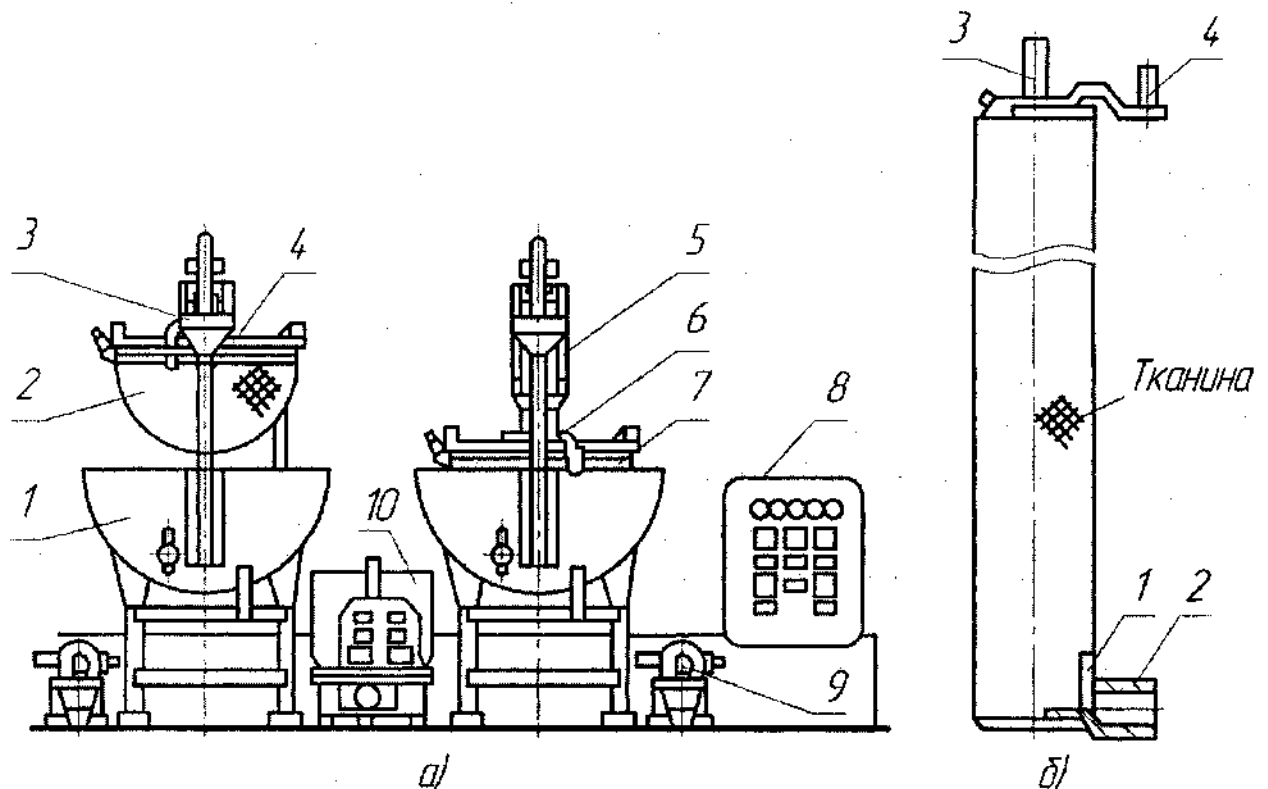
Схема виготовлювача сиру з пресувальними ваннами
